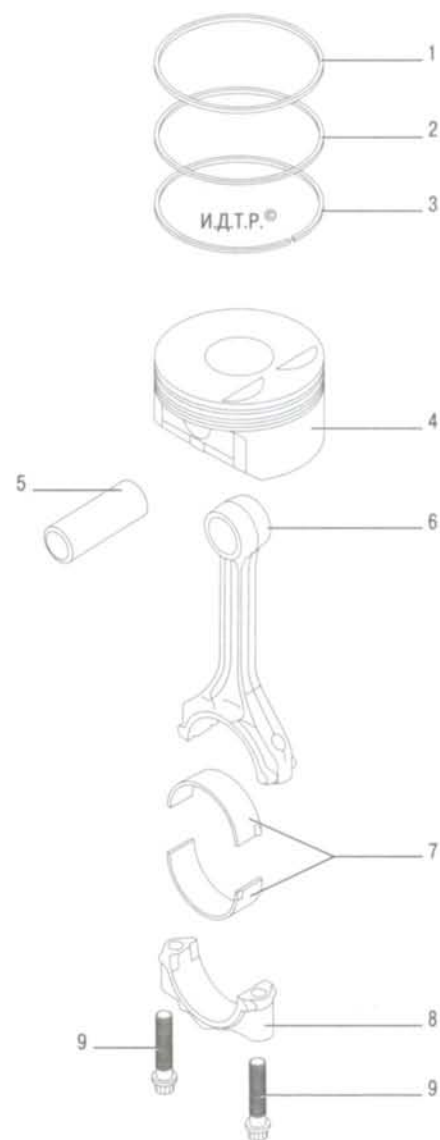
Детали шатунно-поршневой группы: 1 – верхнее компрессионное кольцо; 2 – нижнее компрессионное кольцо; 3 – маслосъемное кольцо; 4 – поршень; 5 – поршневой палец; 6 – шатун; 7 – шатунные вкладыши; 8 – крышка шатуна; 9 – болты крепления крышки шатуна
